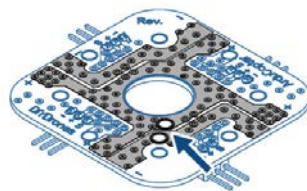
Imagem ilustrativa de como preencher a placa com solda [73]
